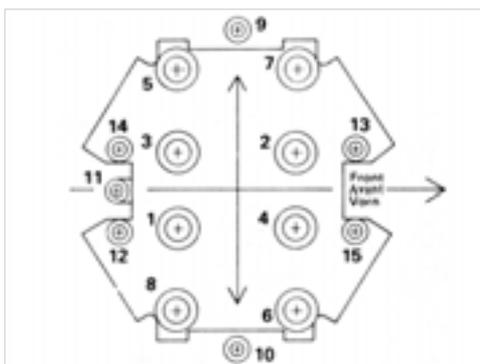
Reihenfolge zum Lösen der Zylinderkopfschrauben
